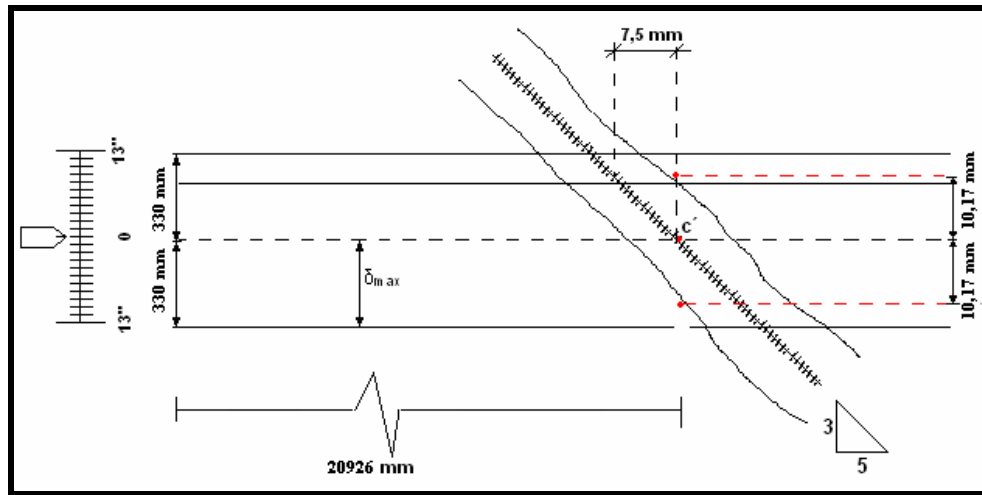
Se representa el ensayo en donde se utilizo el dispositivo láser, para luego trasladar los puntos marcados al cordón de soldadura
